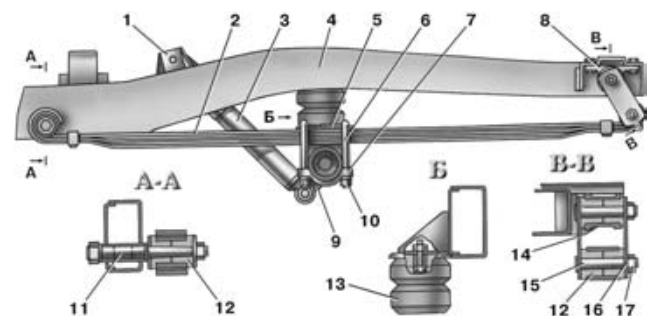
Задняя подвеска с малолистовыми рессорами: 1 - кронштейн амортизатора; 2 - рессора; 3 - амортизатор; 4 - рама; 5 - накладка; 6 - стремянка; 7 - подкладка; 8 - кронштейн серьги; 9 - кронштейн амортизатора; 10 - гайка стремянки; 11 - ось; 12 - втулка резиновая; 13 - буфер; 14 - щека серьги внутренняя; 15 - щека серьги наружная; 16 - щека пальца; 17 - гайка пальца.
